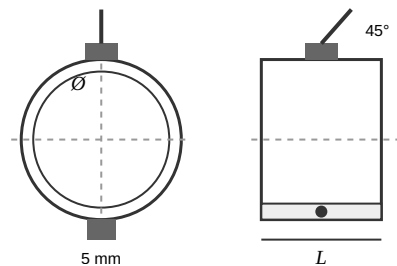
Dimensiones estándar e inclinación del cable a 45°
